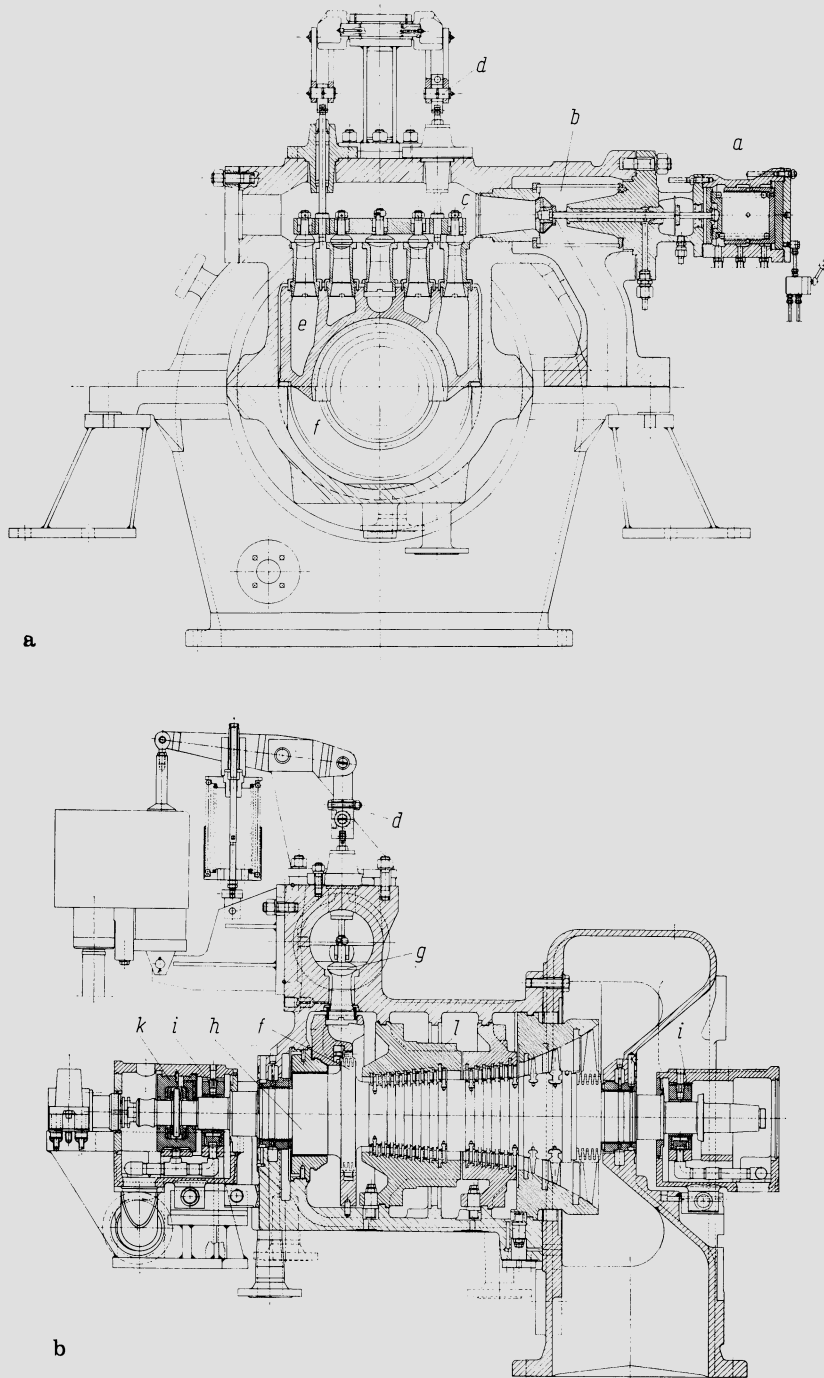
Industrie-Dampfturbine mit Düsengruppenregelung und Stufenüberbrückungsventil für Höchstlast (Siemens) a) Querschnitt; b) Längsschnitt, a) Stellmotor, b) Schnellschlußventil, c) Regelventile, d) Regelventilantrieb, e) Dampfzufuhrkanäle zu Düsengruppen, f) Regelrad, g) Überlastventil
